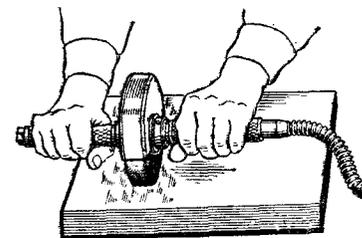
Прием шлифования поверхностей абразивным кругом с приводом от гибкого вала
